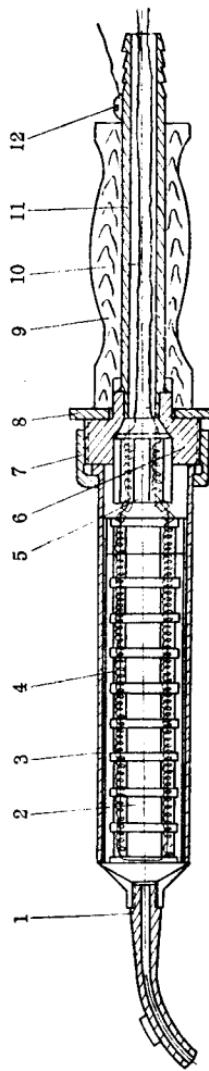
硬聚氯乙烯塑料的焊枪结构
